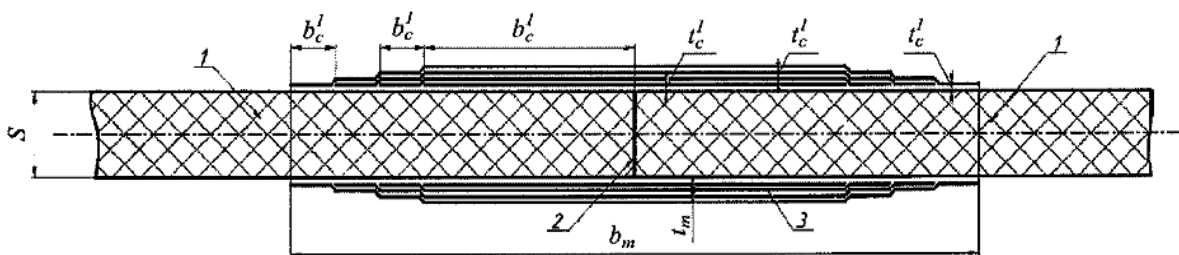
Конструктивна схема стикового (пазового) формованого з'єднання одношарових в'язей без оброблення кромки:
